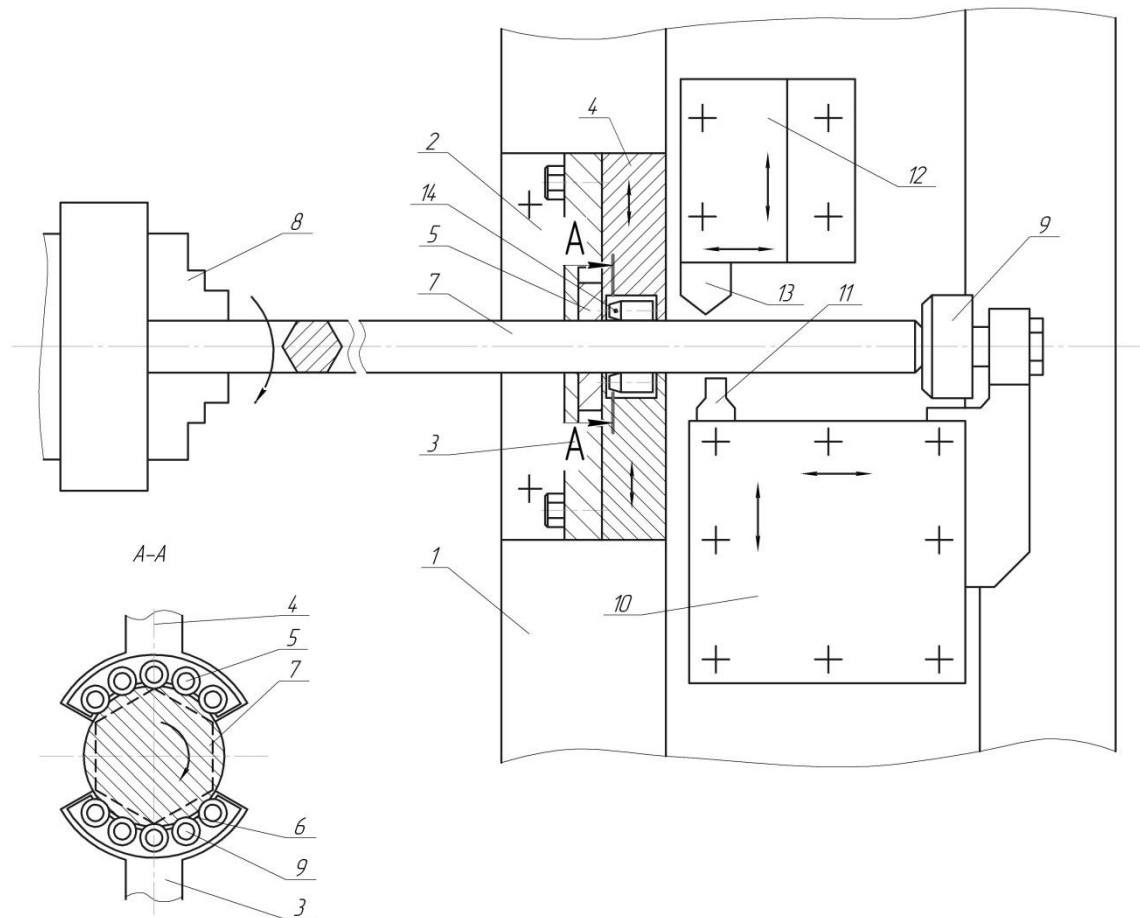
Люнет токарного верстату для відрізання довгомірних заготовок
